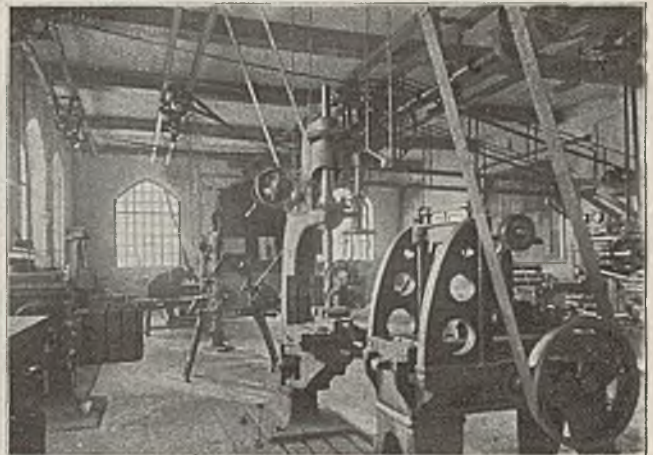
Langhobelmaschine, Querhobelmaschine, drei Bohrmaschinen.
